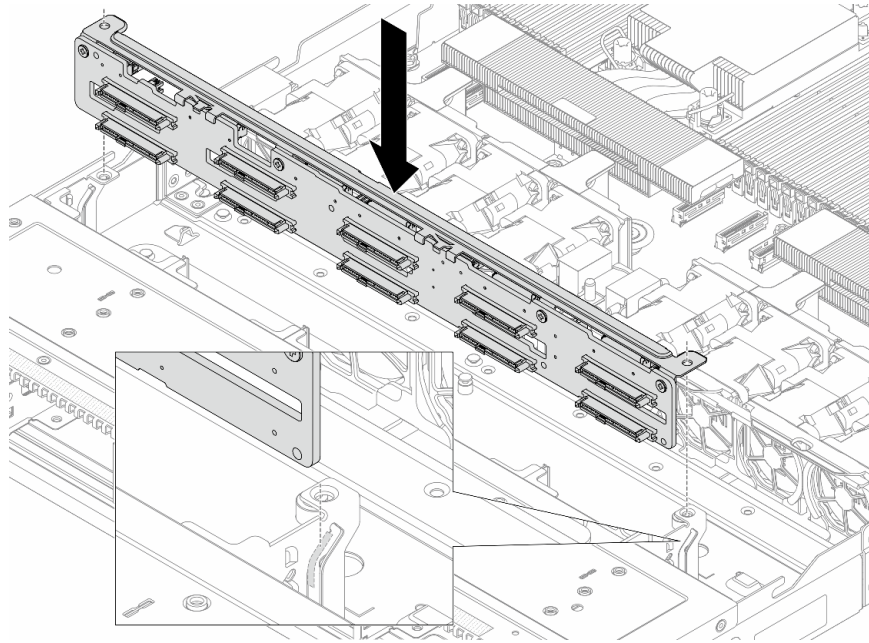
Installation du fond de panier pour dix unités remplaçables à chaud 2,5 pouces
